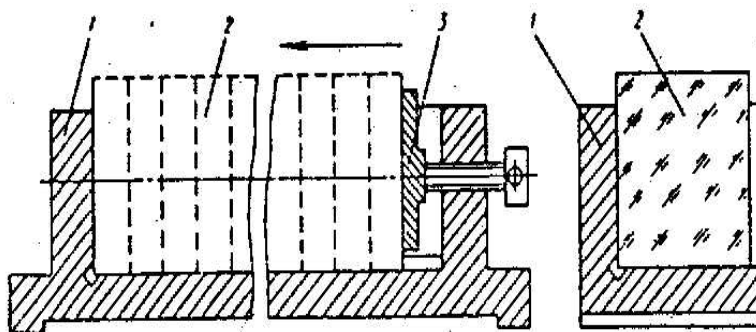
Приспособление для обработки торцов заготовок некруглой формы
